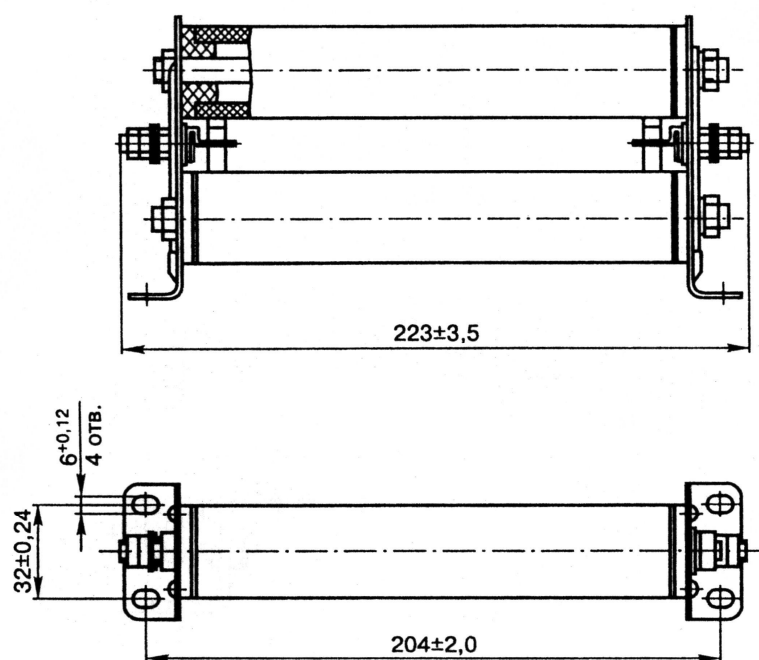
Внешний вид и габаритные размеры резисторов РП
